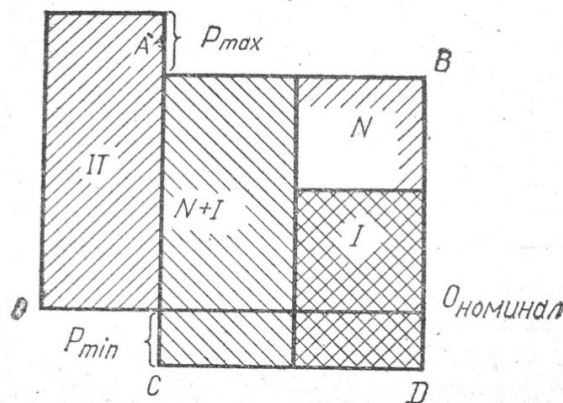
Схема розташування полів допусків розвертки
